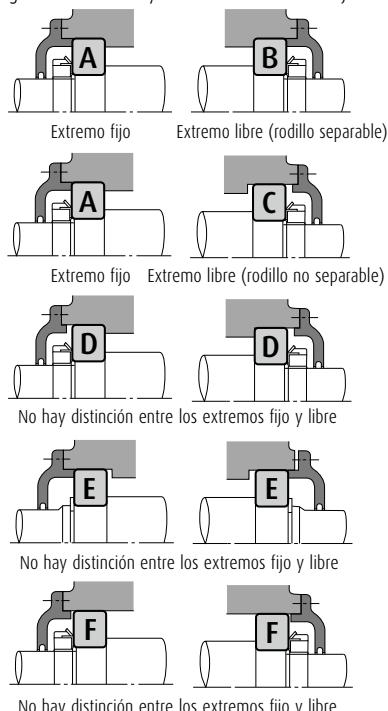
Disposición de montaje y tipos de rodamientos
